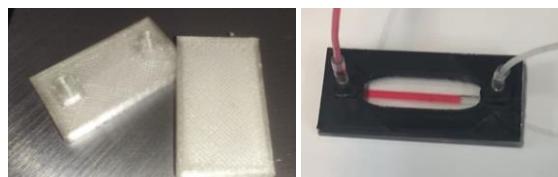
À esquerda está representada a parte superior e inferior de um chip impresso com a técnica FDM com o PETG natural translúcido e a direita, o chip impresso com uma camada em PLA.
